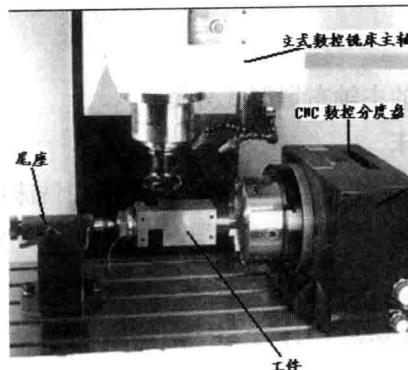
立式数控铣床配数控转盘实现四轴联动加工
